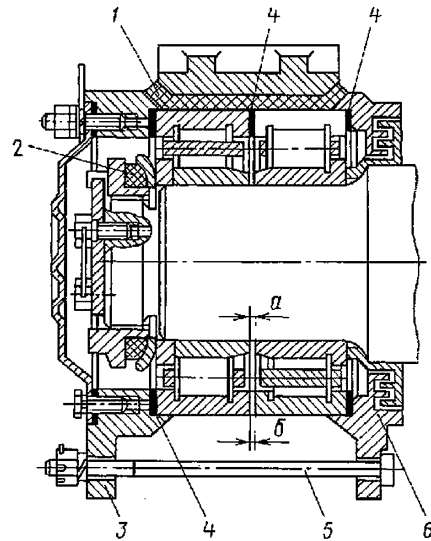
Бескорпусная букса вагона с роликовыми подшипниками:
